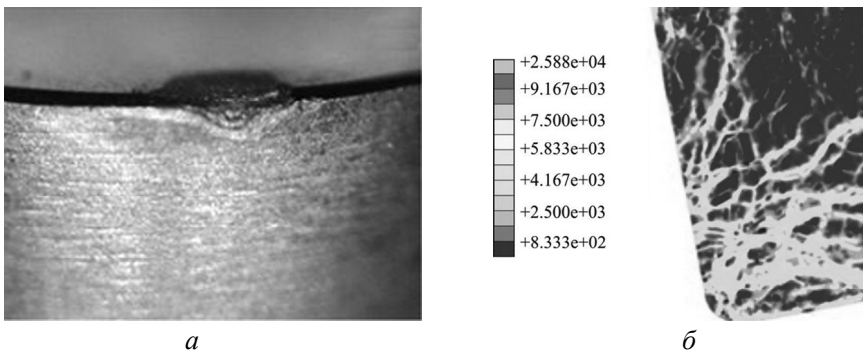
Робоча ділянка різальної кромки інструмента (*a*) та розподіл напружень (*б*) в інструменті з PcBN групи ВН.
